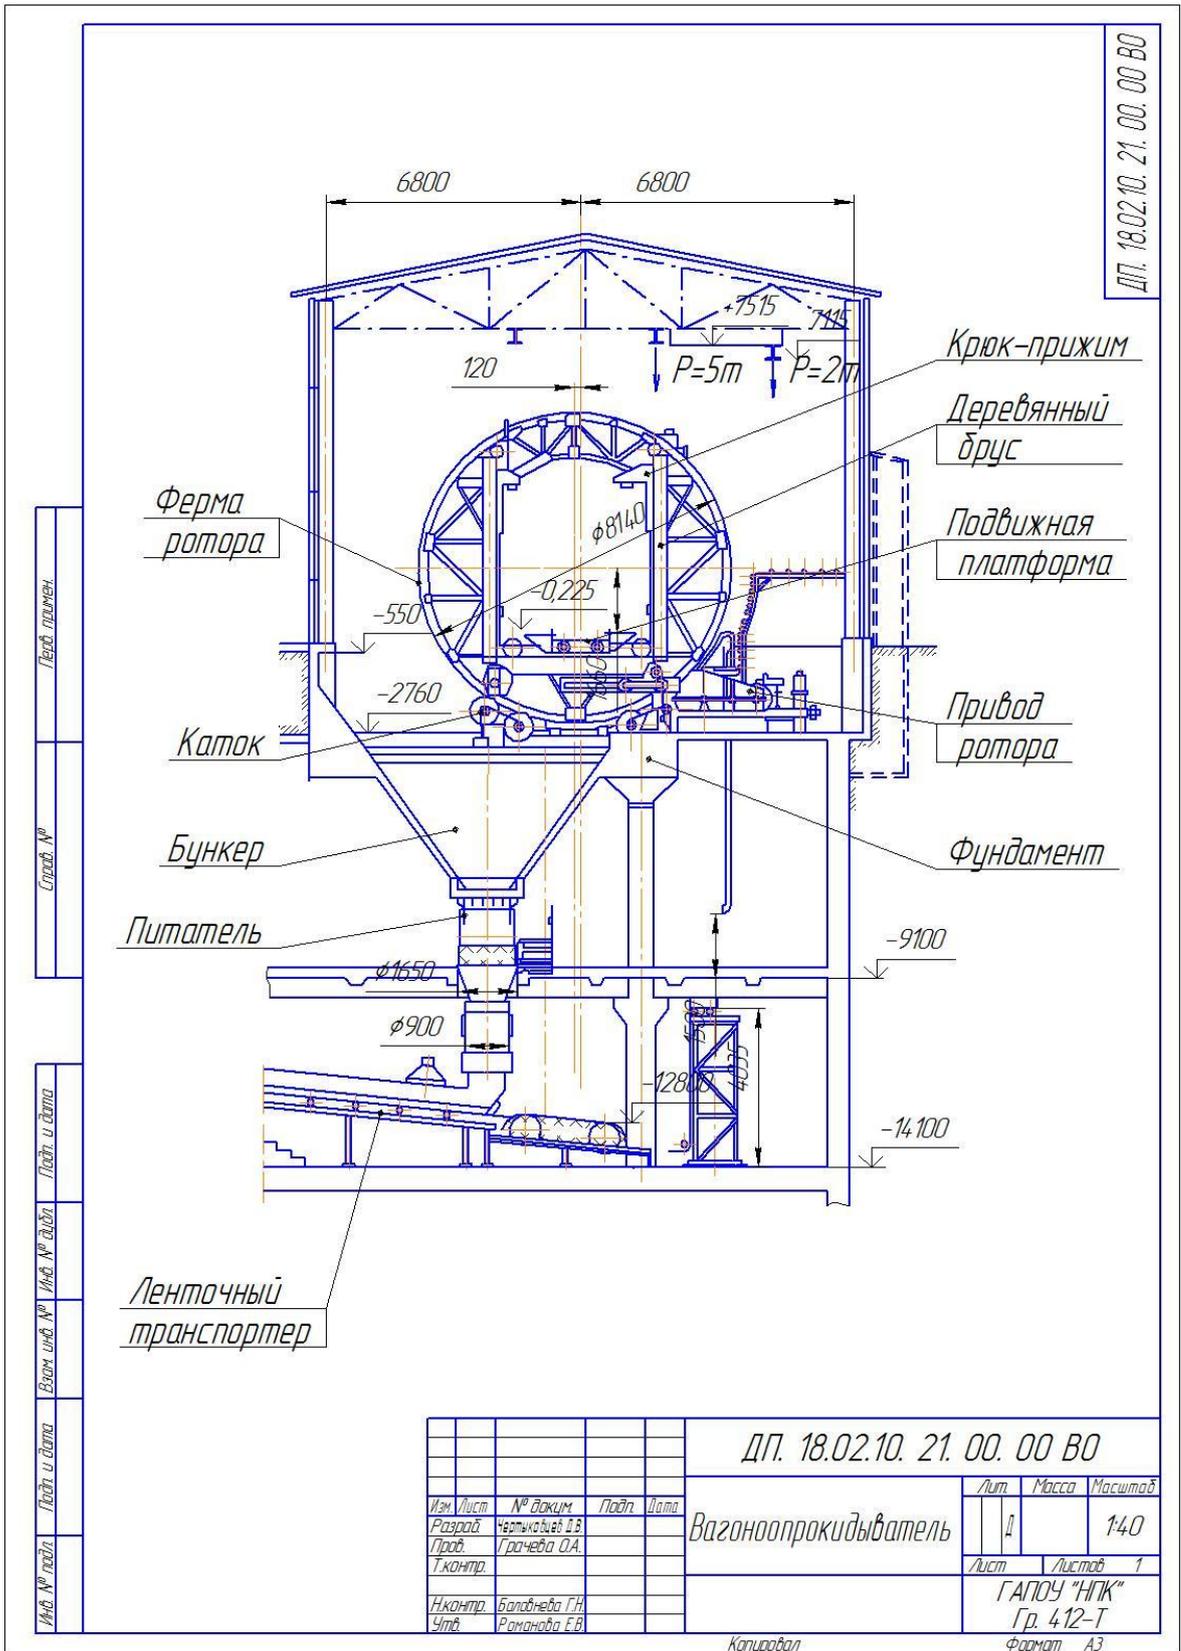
Чертеж вида общего «Вагонопрокидыватель»
